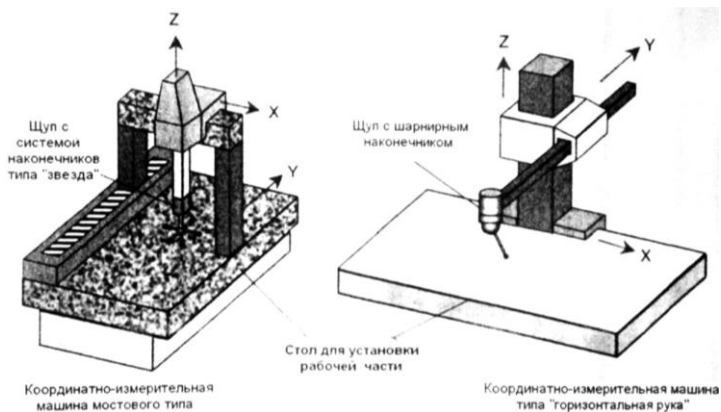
Наиболее часто встречающиеся конструкции координатно-измерительных машин
